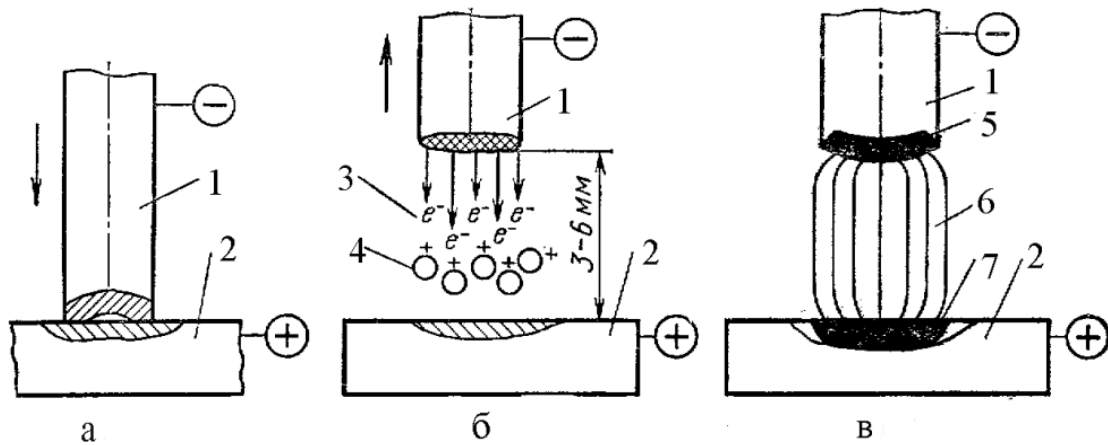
Схема процесса зажигания дуги: 1 – электрод; 2 – свариваемое изделие; 3 – электроны; 4 – положительные ионы (молекулы) газа; 5 – плавящийся конец электрода; 6 – ионизированная сварочная дуга; 7 – сварочная ванна.
